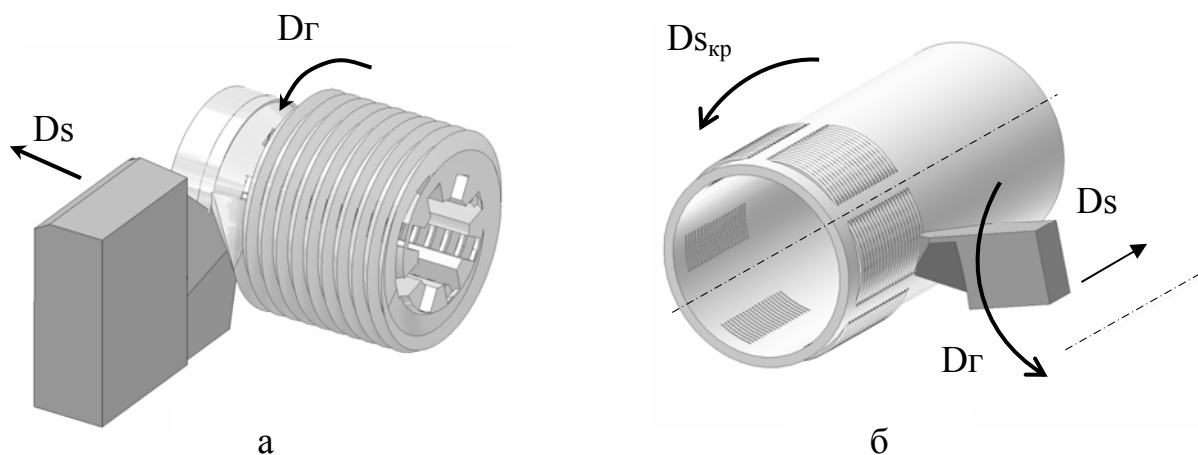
Схемы получения щелевых фильтрующих структур методом деформирующего резания из заготовки с продольными внутренними пазами (а) по токарной схеме и из стандартной трубной заготовки по токарно-фрезерной схеме (б)
